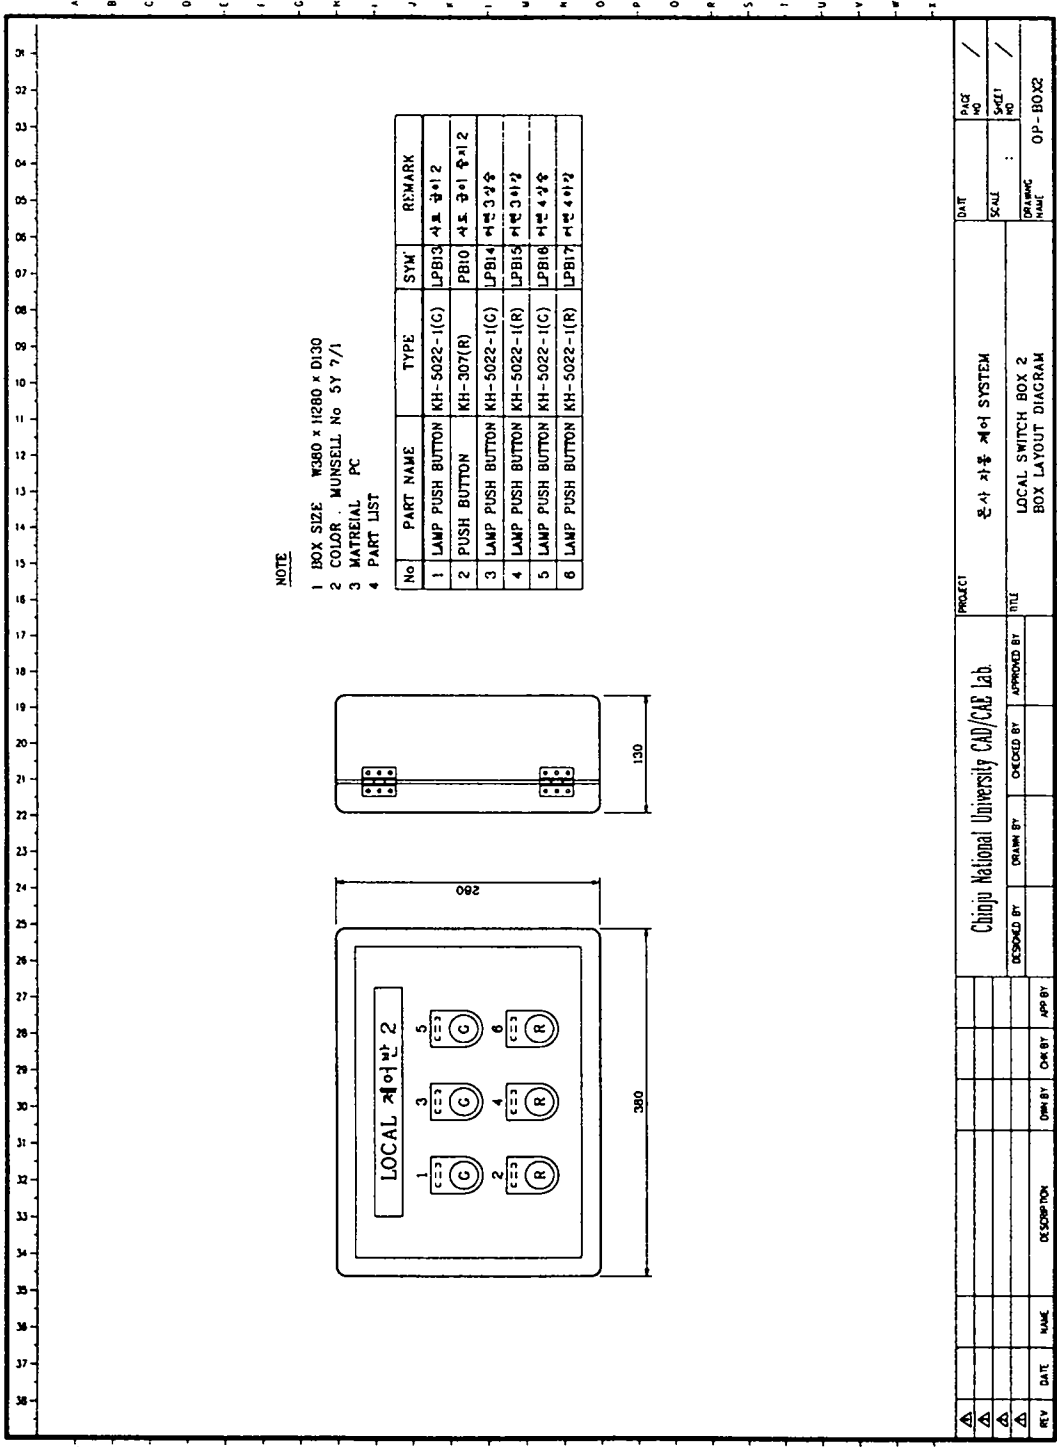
스위치 박스 배치도(Local switch box layout diagram) #2
